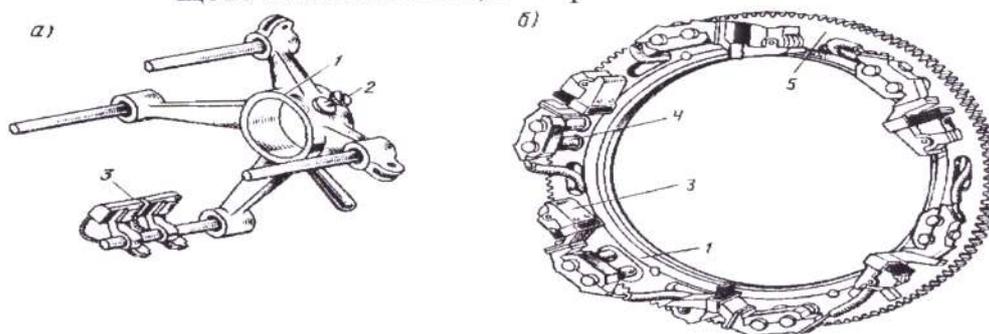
Установка щеткодержателей на поворотной щеточной траверсе: 1 — траверса; 2 — стопорный болт; 3 — щеткодержатели; 4 — палец щеткодержателя; 5 — зубчатый венец
